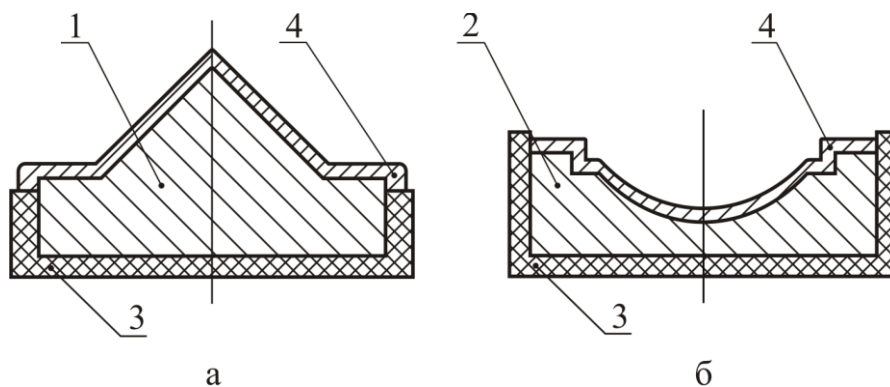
Устройство форм и процесс изготовления масс-анализатора
